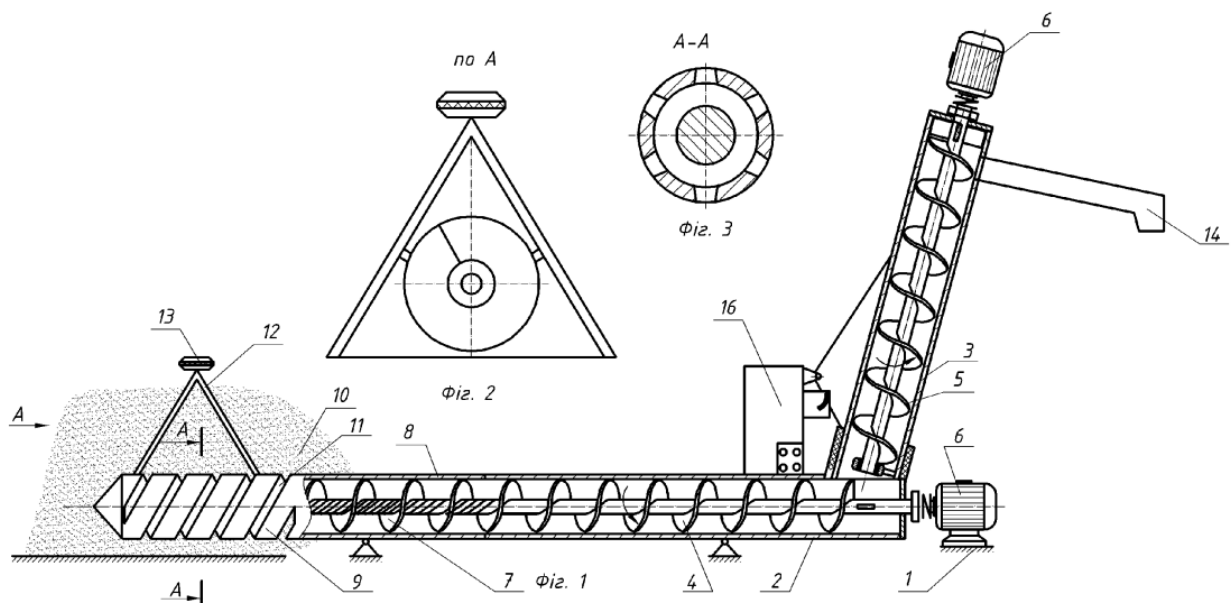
Схема крутопохилого ГК: 1 – рама; 2, 3 – кожух; 4, 5 – шнек; 6 – привод; 7 – гвинтова спіраль; 8 – гнучкий патрубок; 9 – циліндричний наконечник; 10 – вантаж насипний; 11 – наскрізні пази; 12 – опорний пристрій; 13 – регулювальна ручка; 14 – вивантажувальний патрубок.
